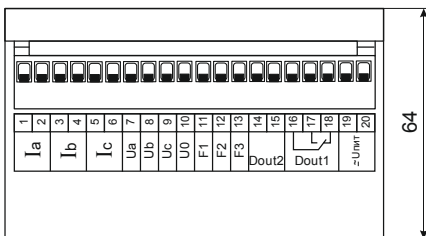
Габаритные и установочные размеры базового модуля ЭКТН ВД.
